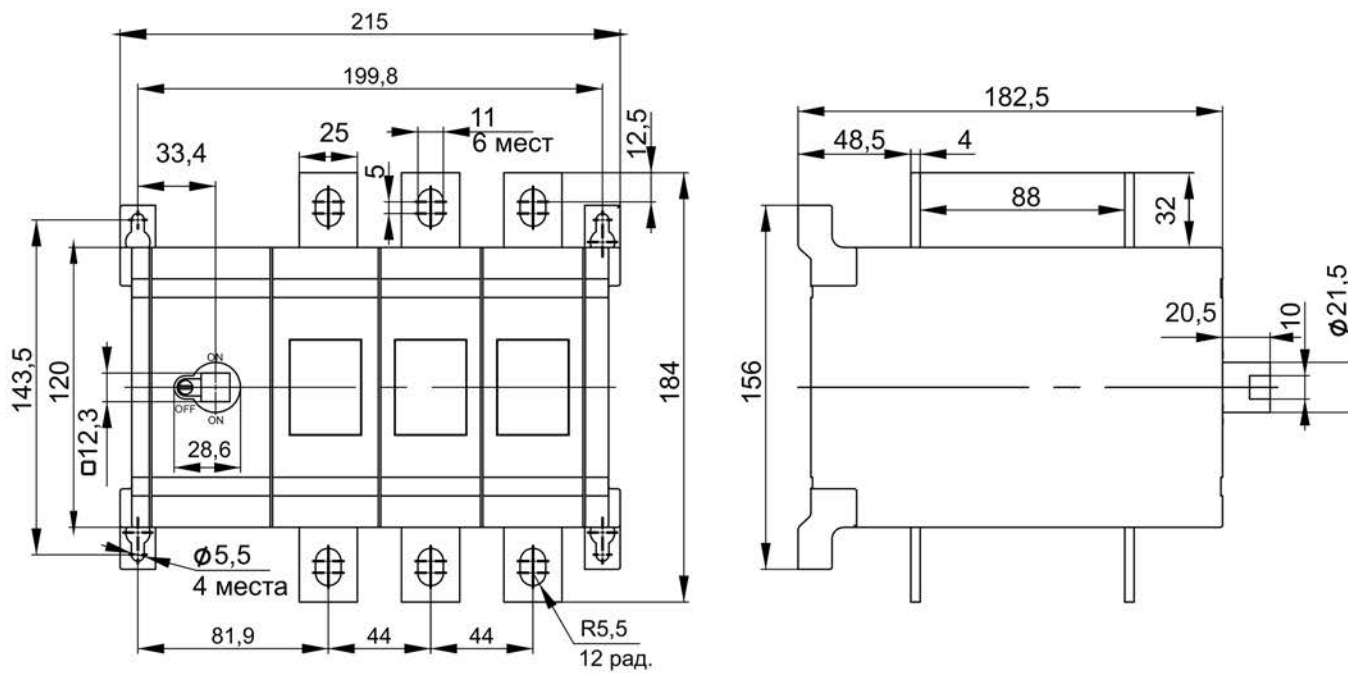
Габаритные, установочные и присоединительные размеры реверсивных ВРК 315–400 А / Figure 6 – Overall, mounting and connection dimensions of reverse VRK 315–400 A
